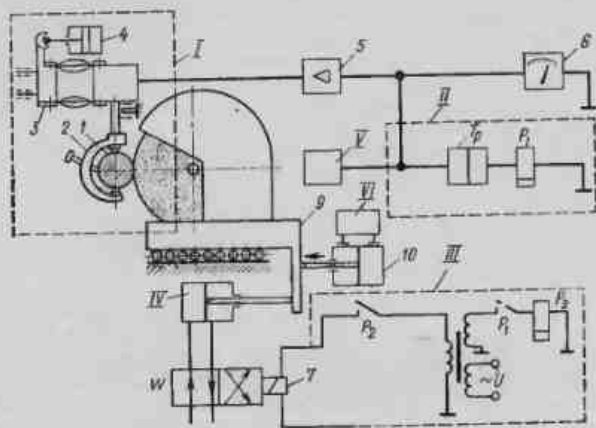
Элементарная схема автоотделителя с исполнительным органом станка: I — обрабатываемая деталь; 2 — головка; 3—4 — подводимое устройство головки; 5 — усилитель; 6 — показывающий прибор; 7 — исполнительный электропривод; 8 — золотник; 9 — каретка шлифовальной бабки; 10 — гидрпривод подачи; 11 — блок головки; III — исполнительный блок станка; IV — гидрпривод быстрого отвода шлифовальной бабки; V — блок питания электросхемы; VI — блок гидравлических подач
